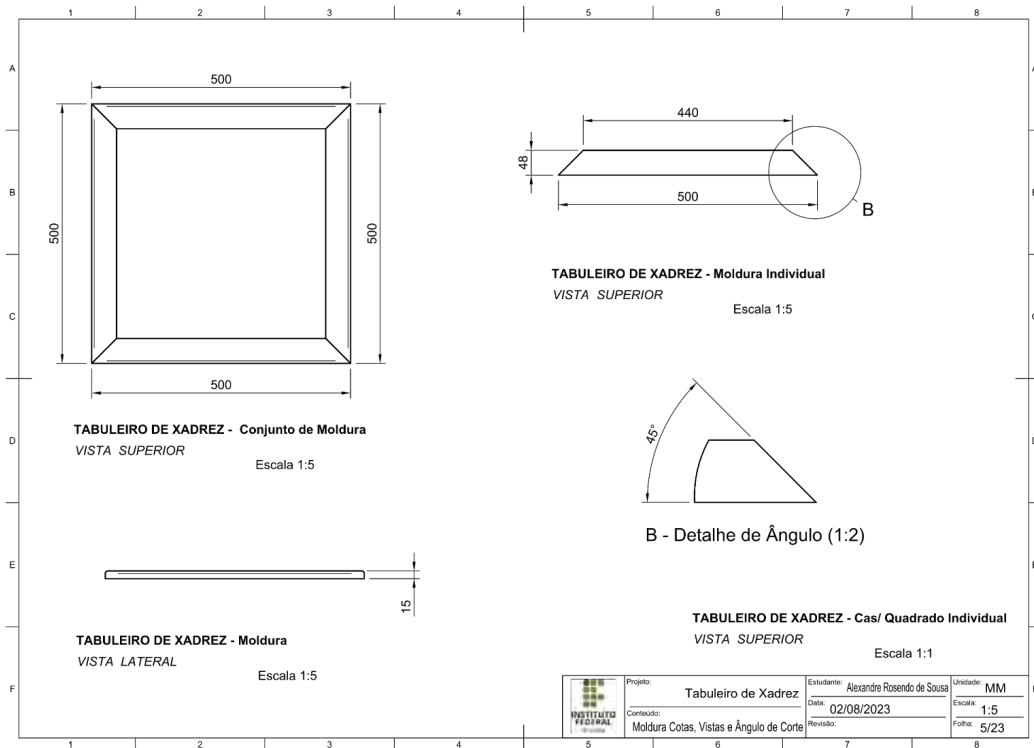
Moldura, Cotas, Vistas e Ângulo de Corte
